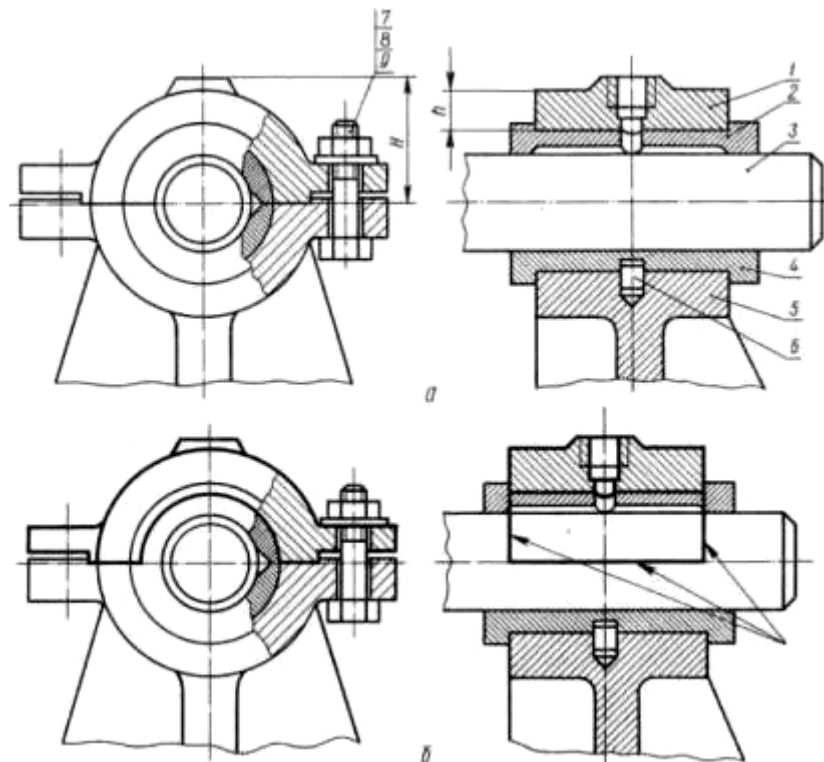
Читання деталей складальної одиниці, контури яких закриті іншими деталями: 1 - кришка; 2 - вкладиш верхній; 3 - вал; 4 - вкладиш нижній; 5 - корпус; 6 - штифт; 7 - болт; 8 - шайба; 9 - гайка
